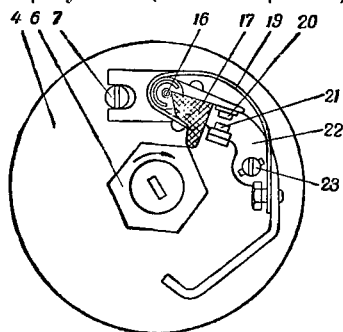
Схема прерывателя (обозначения деталей те же, что и на рис. 75).
